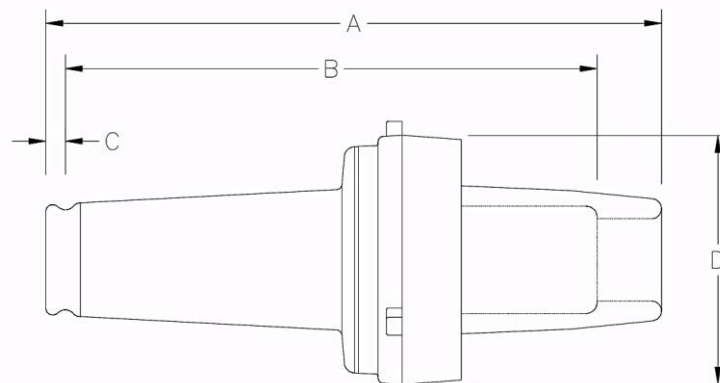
Dimensiones de boquilla tipo inserto, [12].
